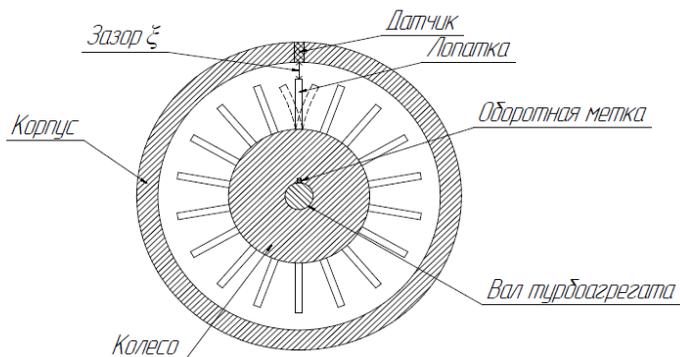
Расположение первичного преобразователя в корпусе турбоагрегата
